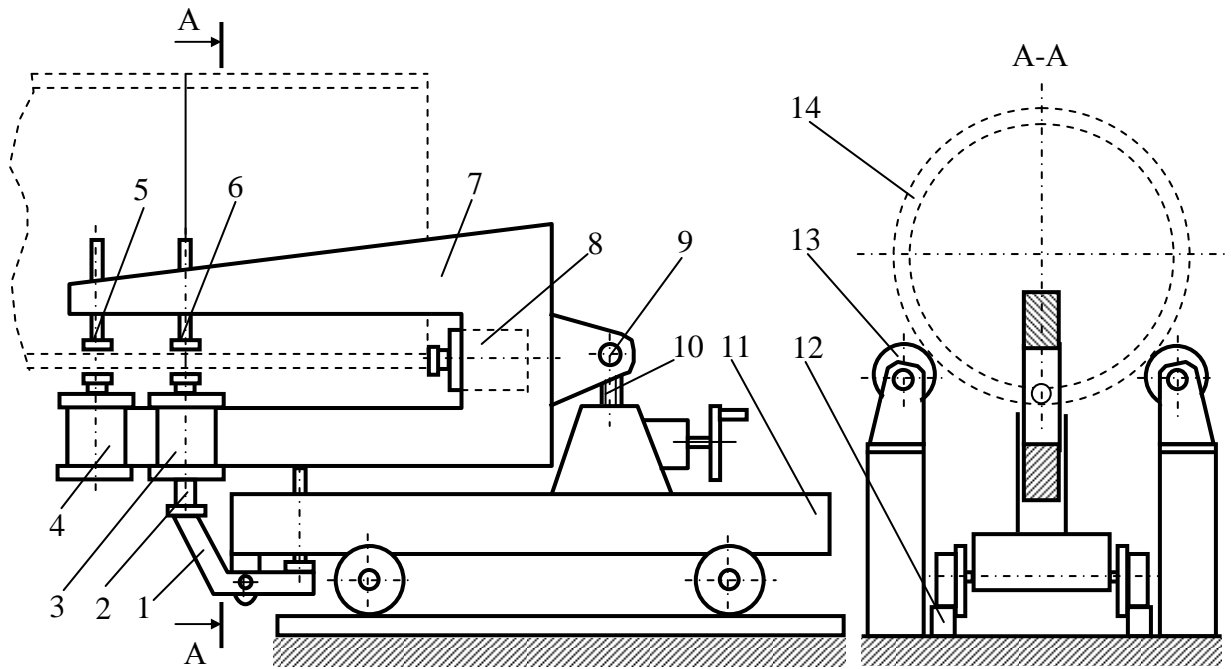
Пристрій для складання обичайок по кільцевим стикам: 1-опора регульована; 2-шток; 3, 4-пневмоциліндри; 5, 6-опори регульовані; 7-скоба; 8-гідроциліндр; 9-вісь; 10-гвинт; 11-візок; 12-рейки; 13- роликовий стэнд
